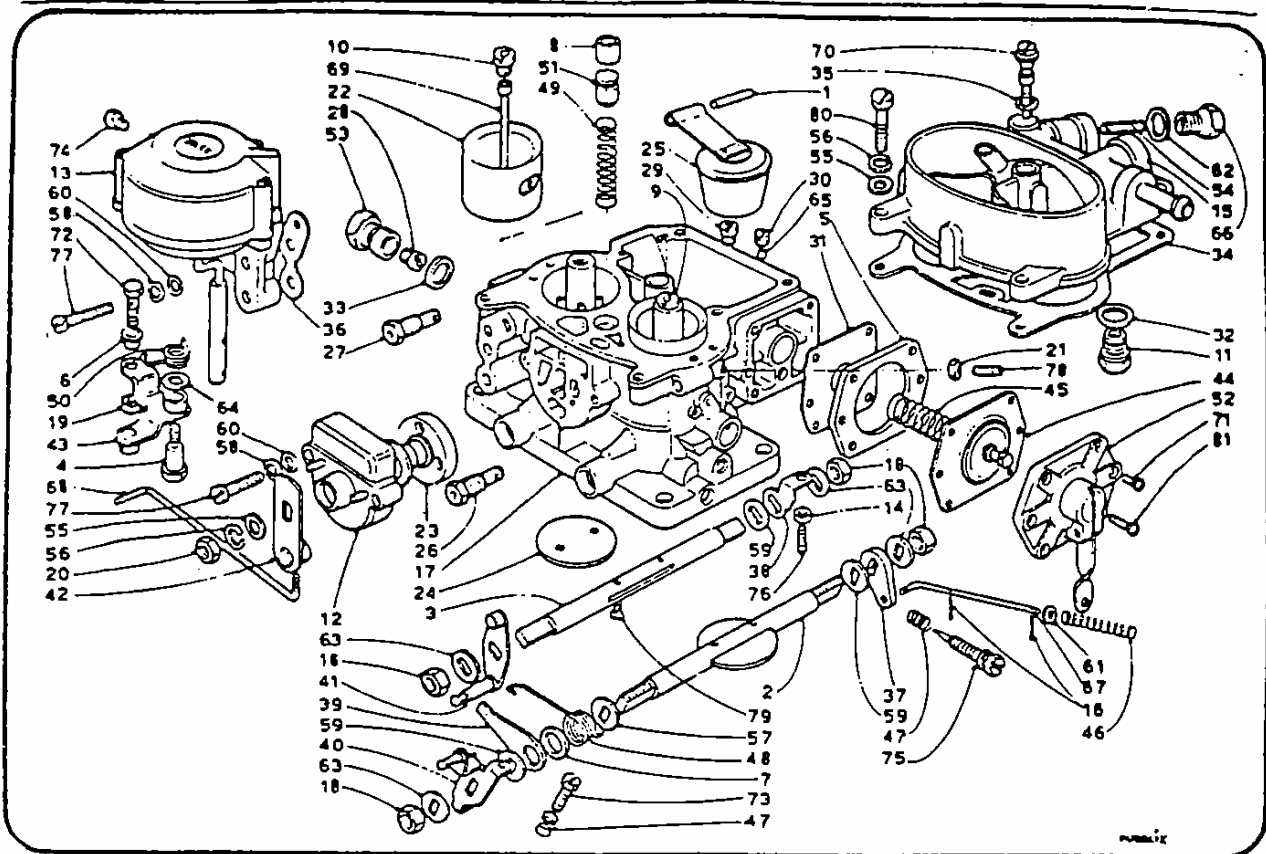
/43 - Carburateur (du Catalogue Pièces Détachées).
